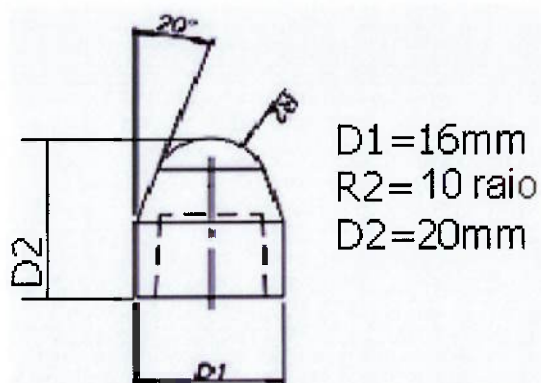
Geometria e dimensões do eletrodo de face esférica de contato.
